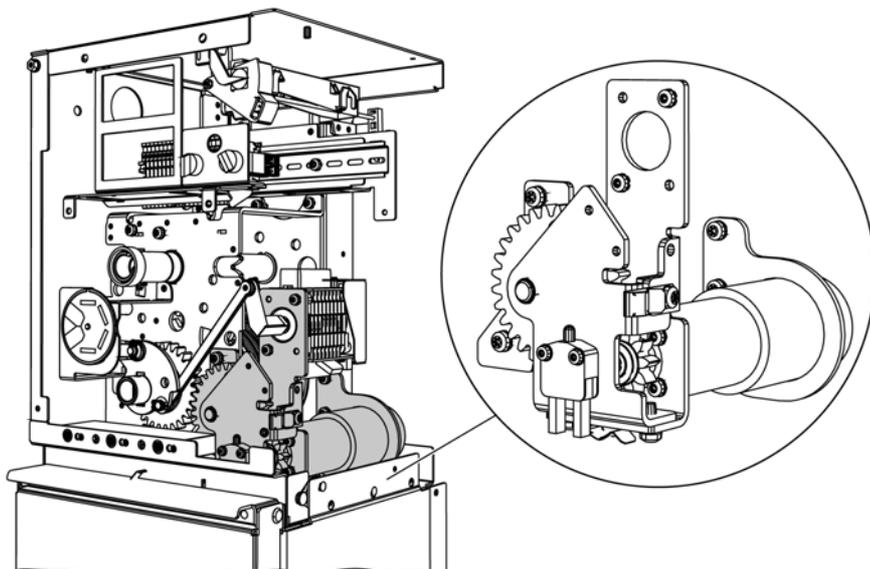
Электромоторный элемент пружинно-скачкового привода в ячейке кольцевого кабеля
